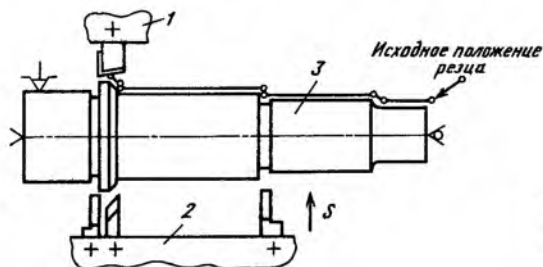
Схема наладки токарного гидрокопировального полуавтомата для обработки ступенчатого вала
